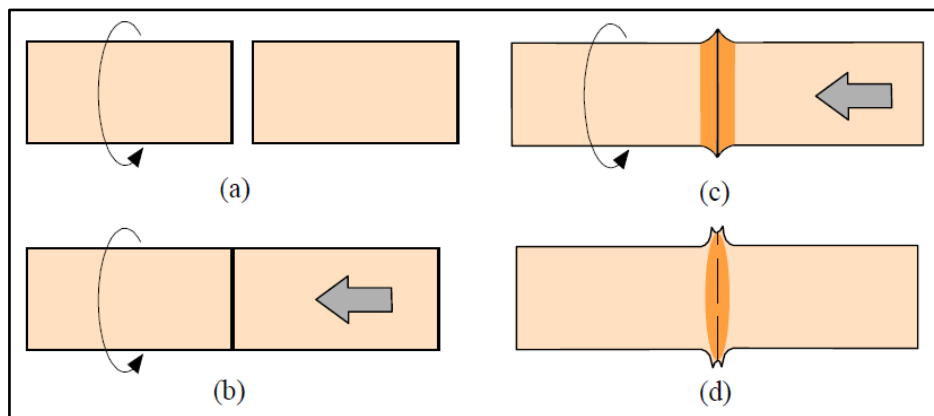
Soldadura por fricção: rotação (a), compressão (b), aquecimento (c) e fusão (d) [9].
